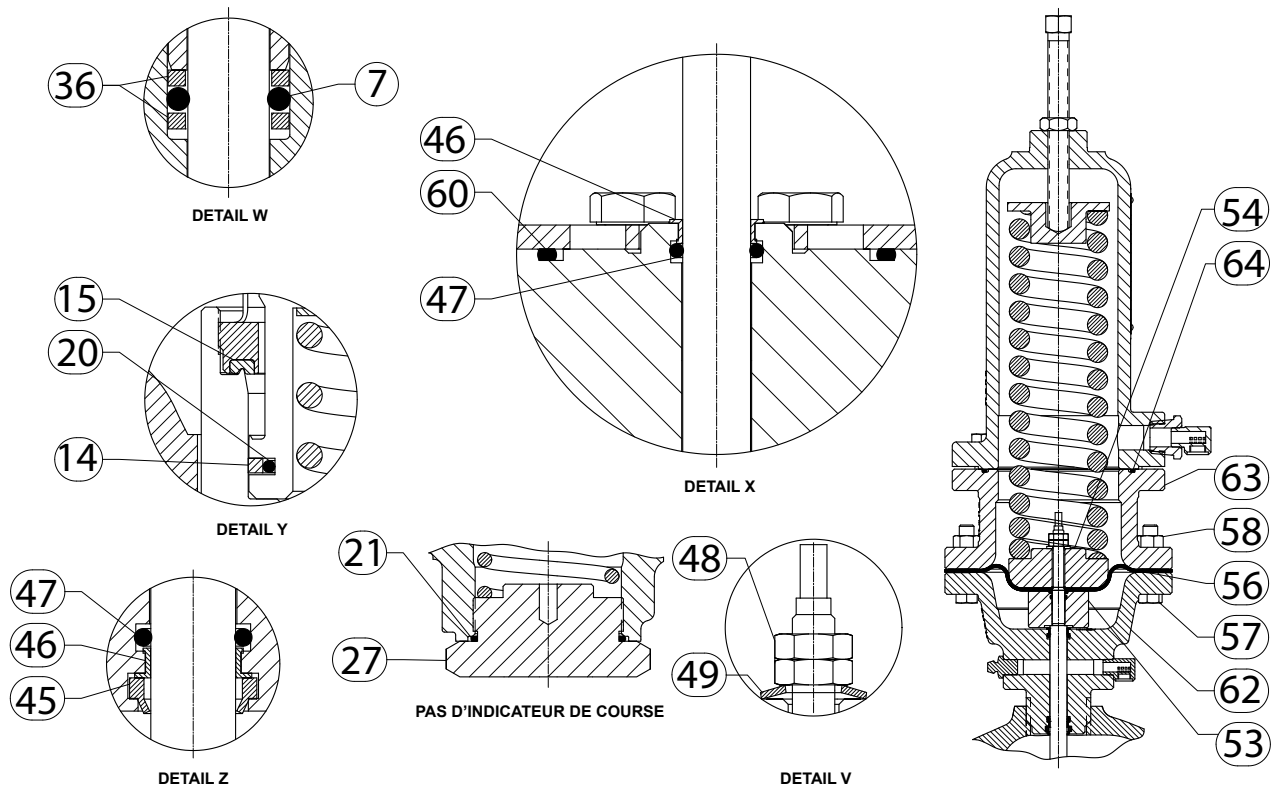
Dessins d'assemblage pour le Type MR105 (suite)
